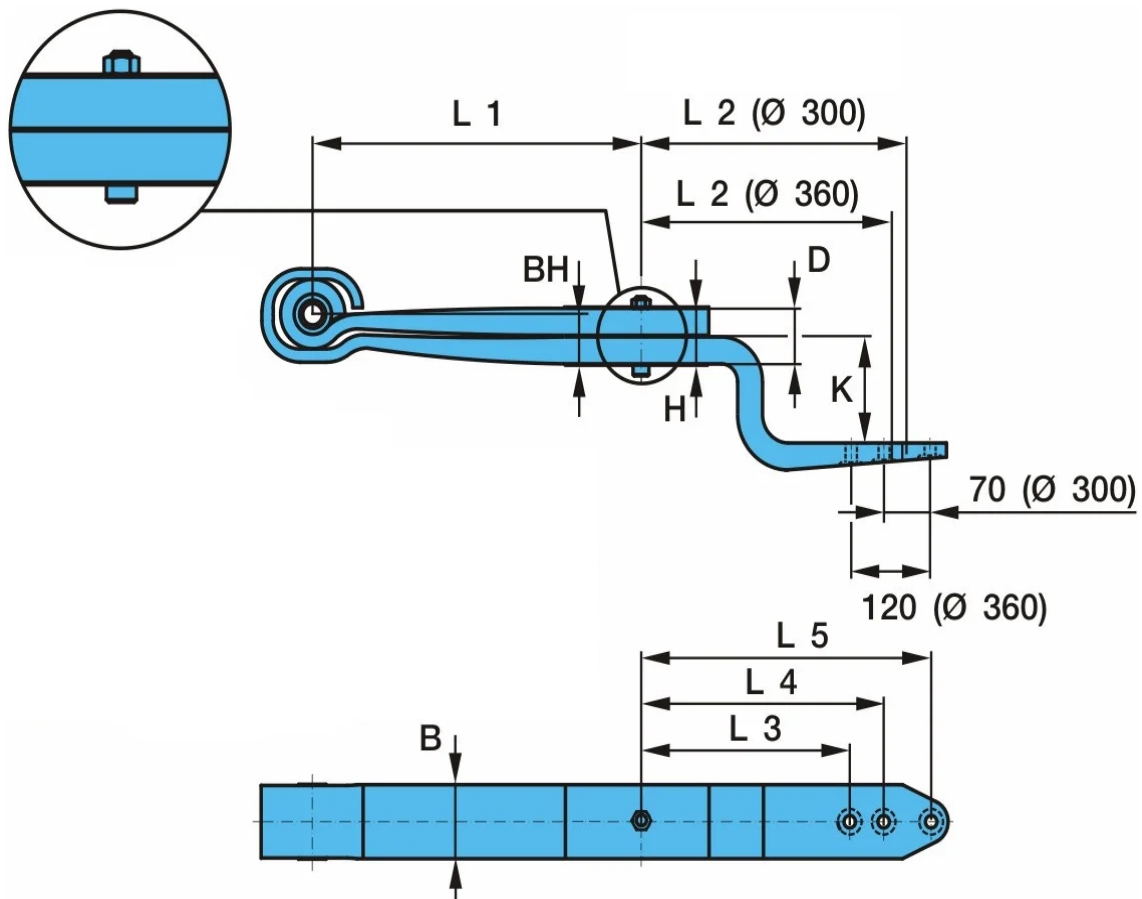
Конструкційна схема 2-х листової напівресори фірми BPW
